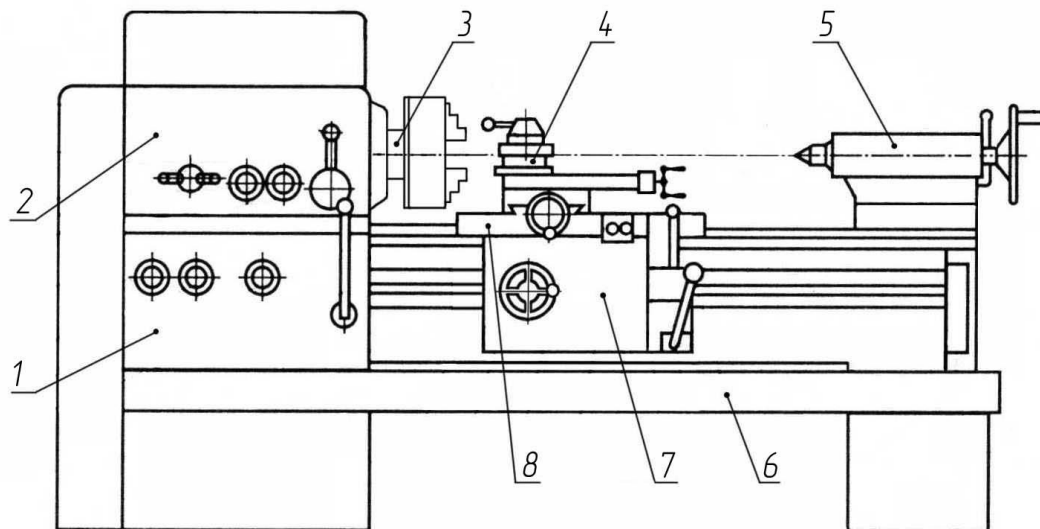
Схема токарно-гвинторізного верстата 16K20
